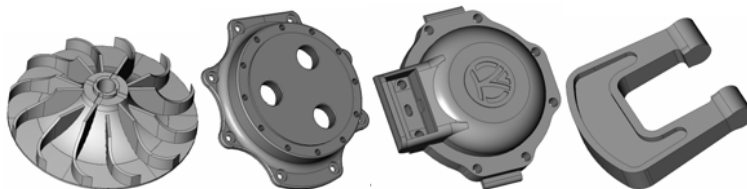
Детали-представители: колесо турбокомпрессора, корпус, крышка, скоба
